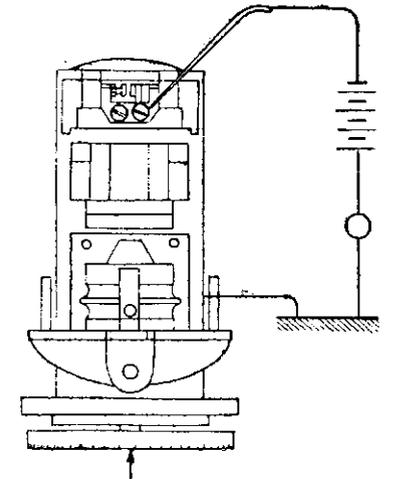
Схема установки для проверки прерывателя Сцинтилла.
